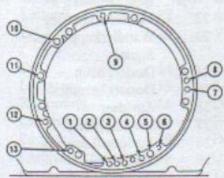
Pumpen-an-Gehäuse-Ölkanäle
